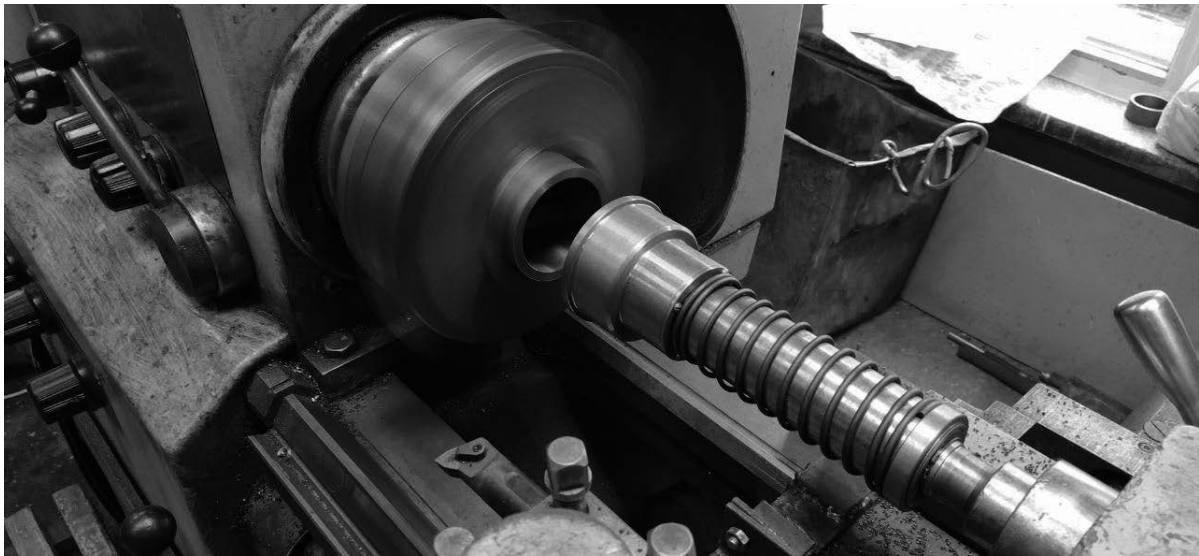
ИИО заготовки на станке 16K20ПФ1
